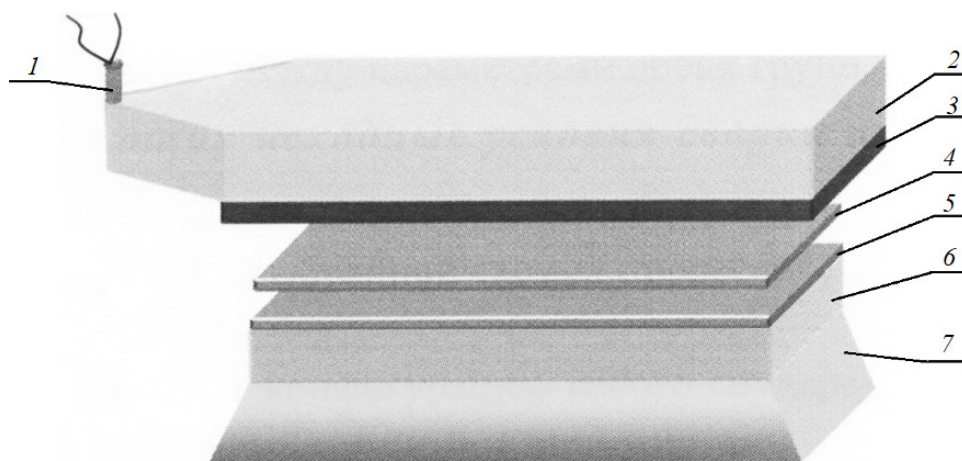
Схема сварки композиционного материала взрывом: 1 – электродетонатор; 2 – контейнер с взрывчатым веществом; 3 – метаемая пластина; 4 – промежуточная пластина; 5 – неподвижная пластина; 6 – металлическое основание; 7 – грунт
